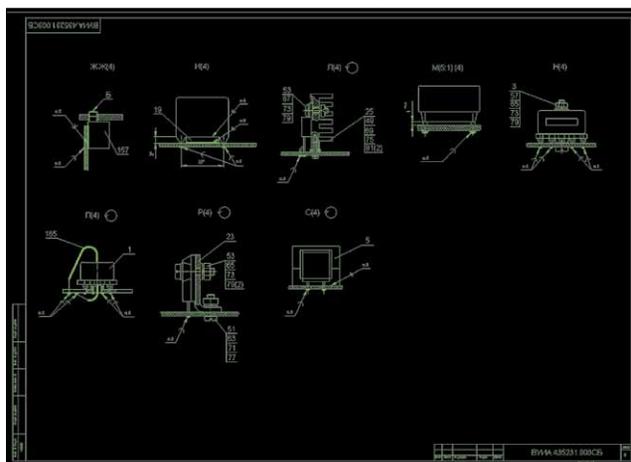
Продолжение размещения (вариант 2) на листе 2 сборочного чертежа печатной платы (слой TOP Assy – зеленый цвет)
